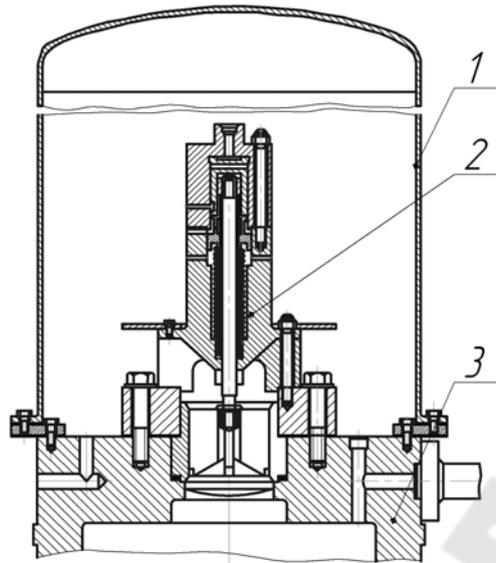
Наполнительный бак и клапан: 1 – наполнительный бак; 2 – наполнительный клапан; 3 – рабочий цилиндр
